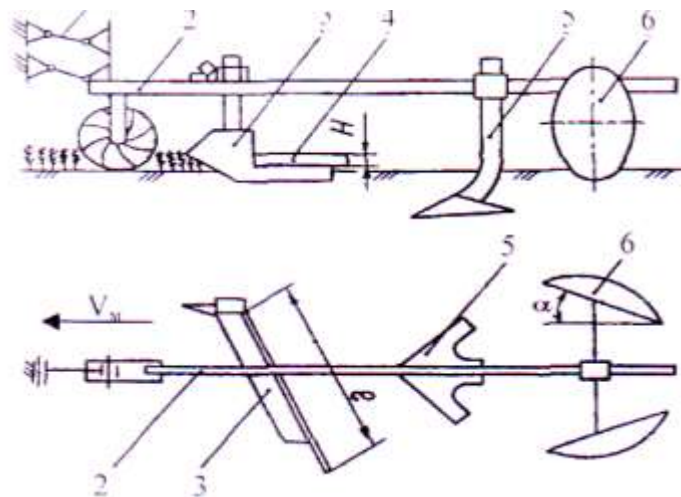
Секция рабочих органов для полосной обработки почвы: 1-механизм навески; 2-грядил; 3- плоскорежущая лапа; 4-почвосдвигающая пластинка; 5-стрельчатая лапа; 6-дисковый рыхлитель.
